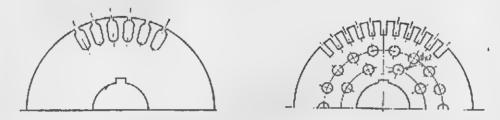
Лист сердечника якоря с овальными полузакрытыми пазами.
